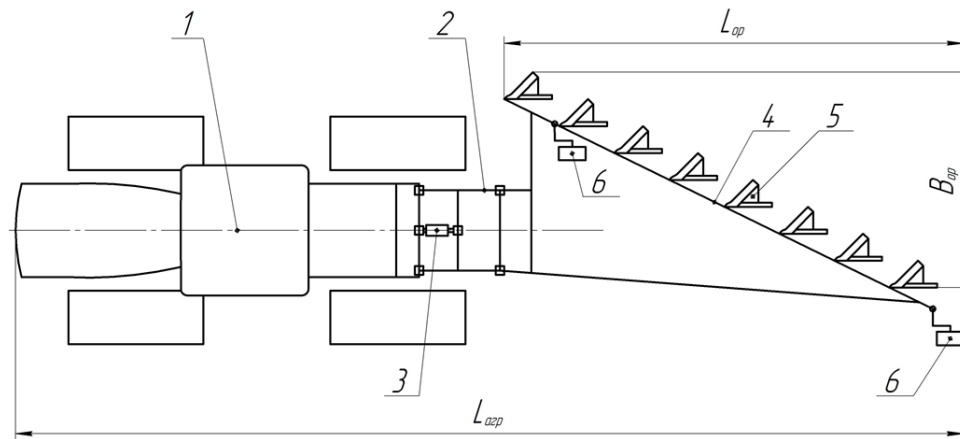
Принципиальная схема пахотного агрегата, комплектованного лемешно-отвальным плугом ПНЛ-8-35 со стойками СИБИМЭ (с корпусами ЛП-0,35): 1 – трактор; 2 – навеска; 3 – гидроцилиндр; 4 – рама орудия; 5 – рабочий орган; 6 – опорные колеса.
